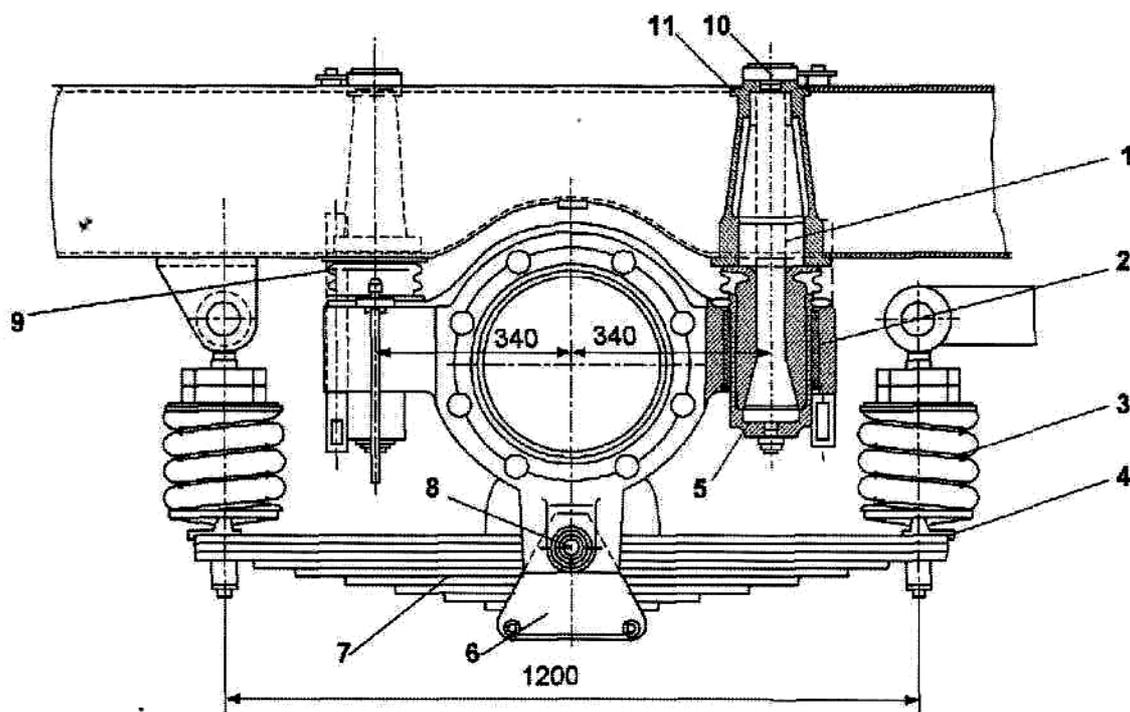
Буксовый узел с цилиндрическими направляющими электровоза ЧС-2: 1-шпинтон; 2-резинометаллический блок; 3-пружина; 4-опора; 5-стакан; 6-щека; 7-рессора; 8-валик; 9-гармошка; 10-гайка; 11-основание.
